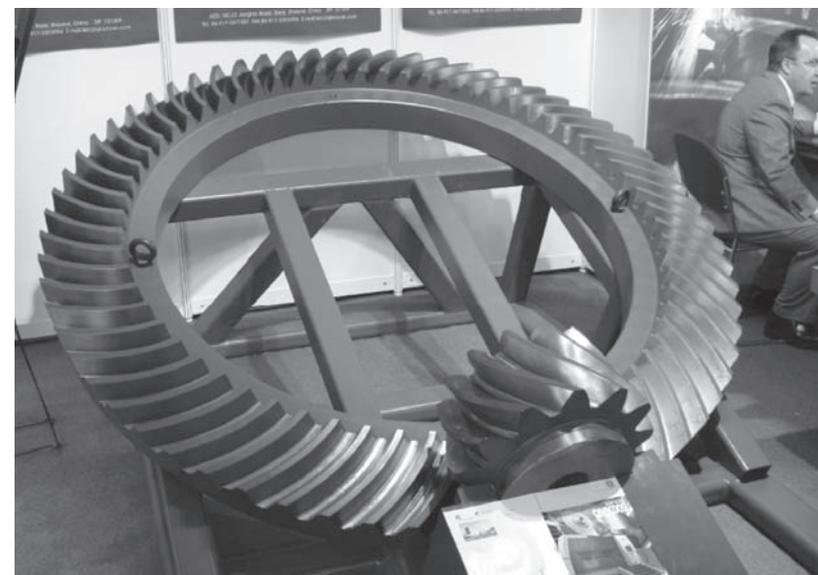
Engranaje de grandes dimensiones de tipo espirocónico
